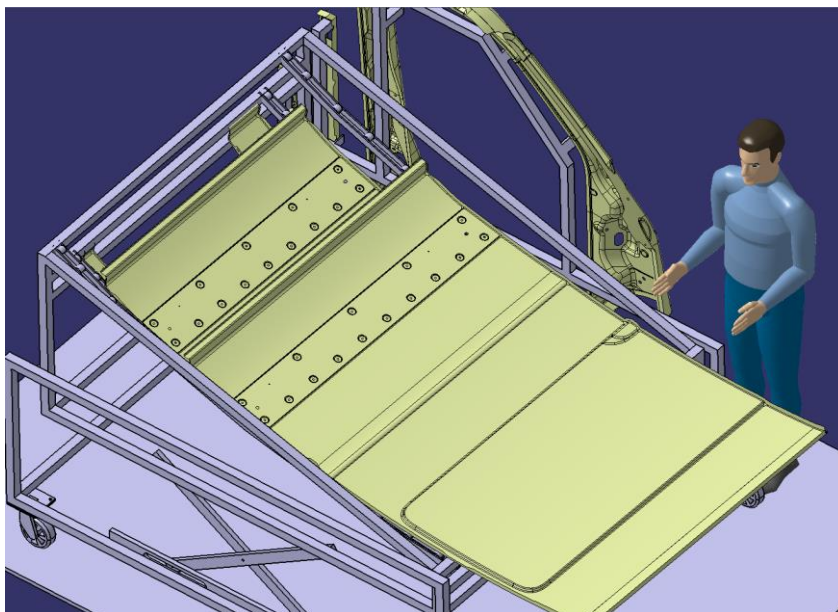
Exemplo de Sistema de Elevação Tesoura
